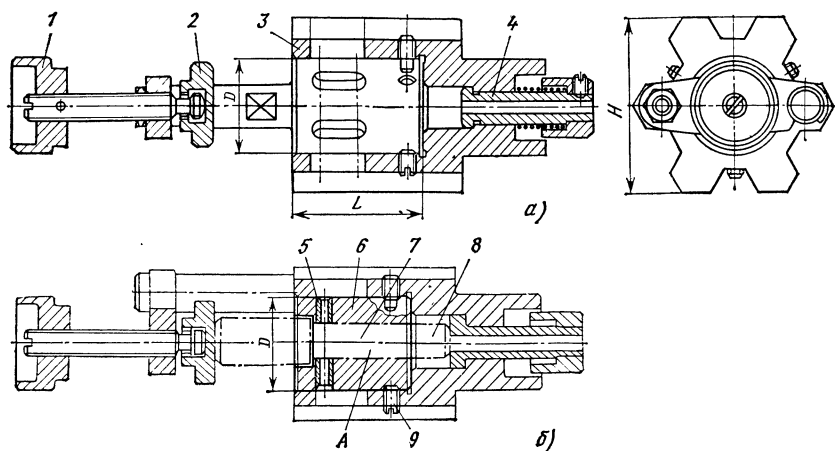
Переналаживаемый кантующийся кондуктор для сверления трех и шести равно расположенных отверстий
